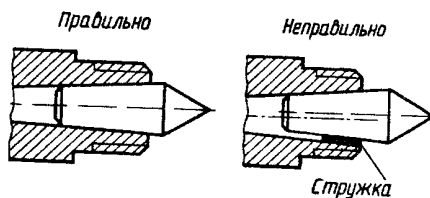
Установка жорсткого центру в шпинделі токарного верстата
